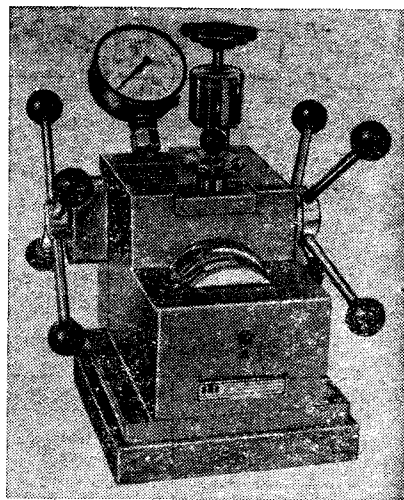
Прибор для испытания на скручивание плоской заготовки
